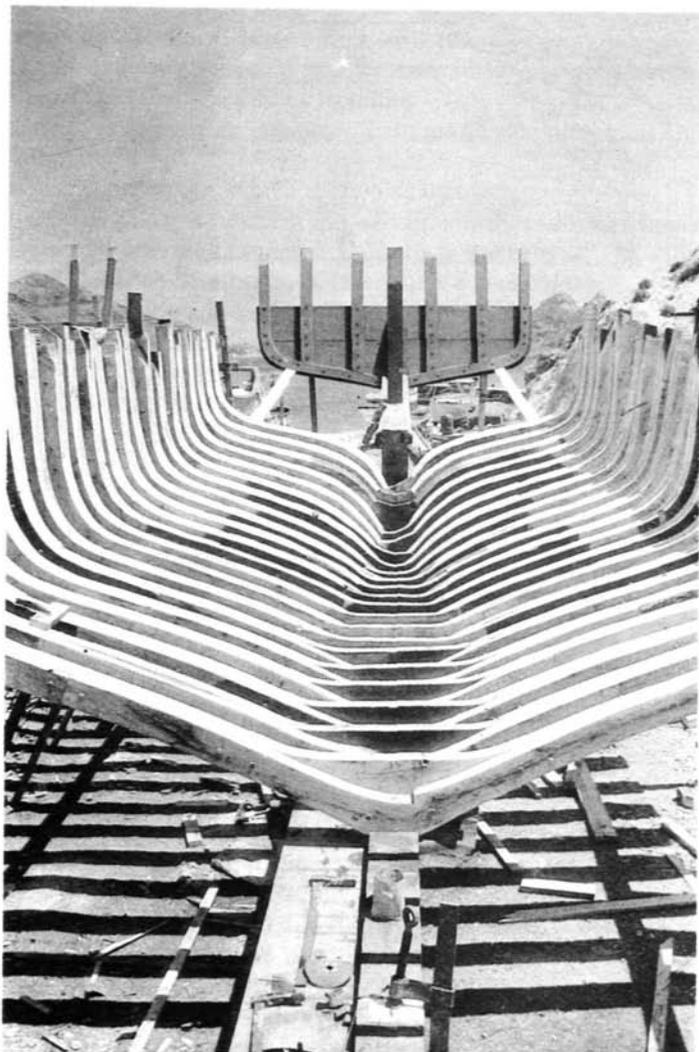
Armazón de cuadernas dobles en una embarcación artesanal actual.(Foto C. León)
